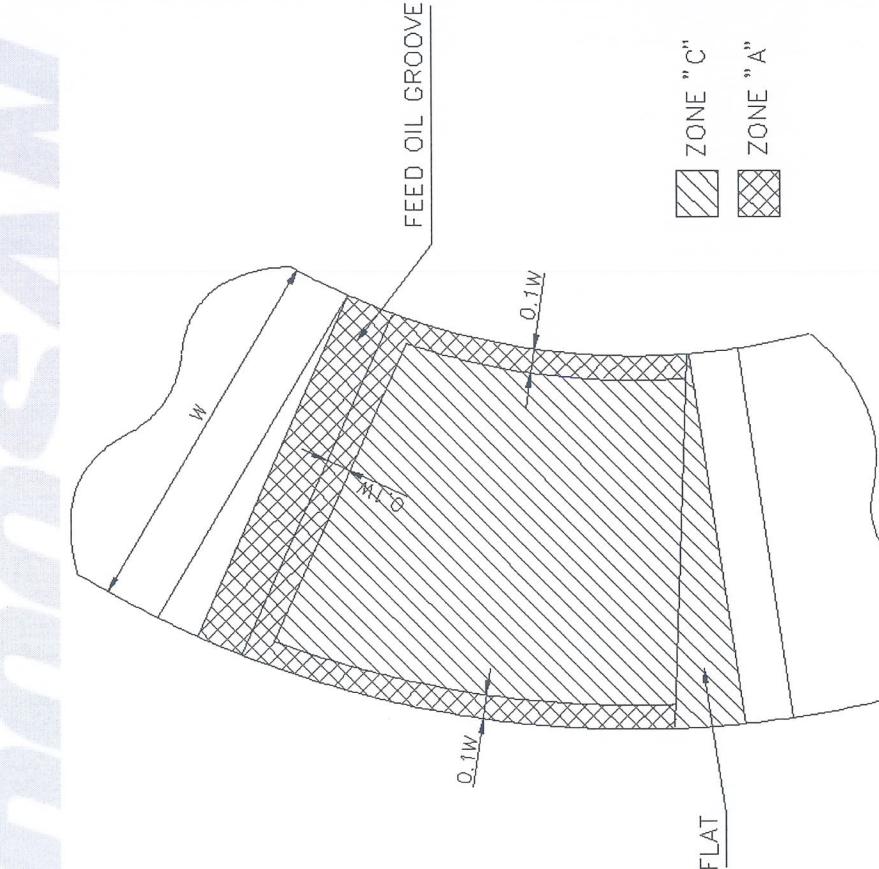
THRUST BEARING 의 BABBIT 구역 표준 구분도
